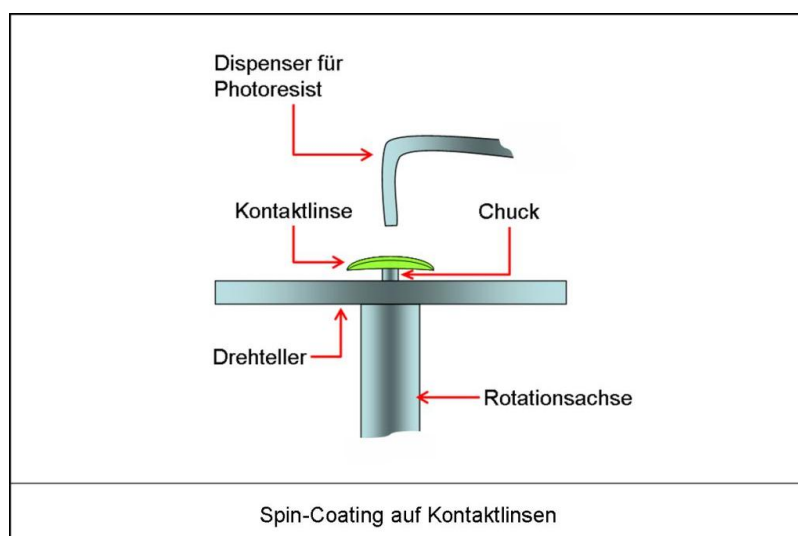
Die Zeichnung zeigt den schematischen Aufbau für die Beschichtung der Kontaktlinse mit dem Photoresist mittels Spin Coating.
